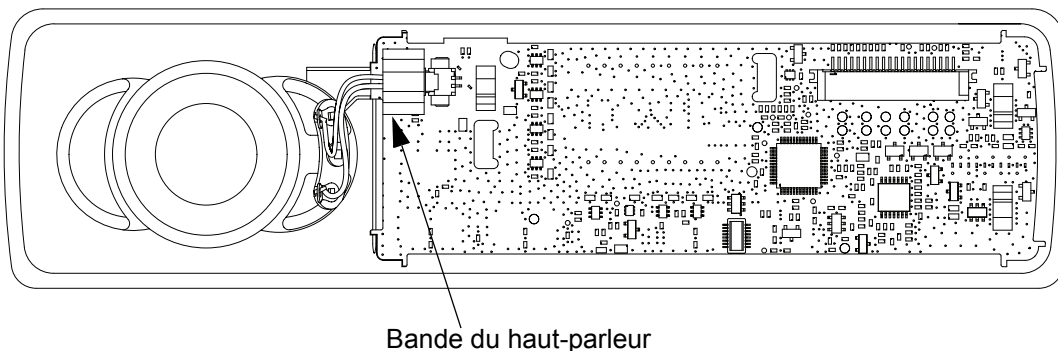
Assemblage de la bande du haut-parleur sur la carte à circuit imprimé
